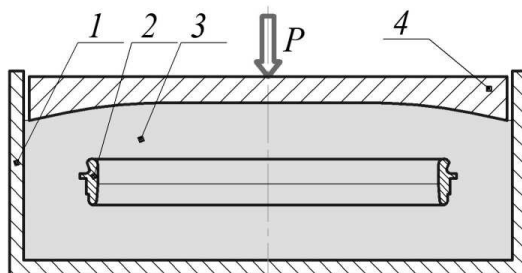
Принципова схема пристрою для ізостатичного ППД: 1 – робоча камера; 2 – деталь; 3 – сферичні індентори; 4 – поршень
